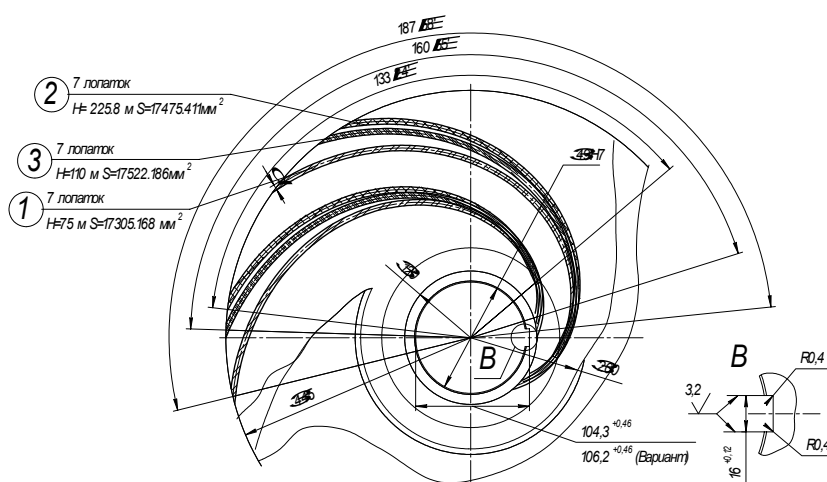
Планы лопастей рабочих колес насоса типа АЗЕ-630.75, АЗЕ-630.110 и АЗЕ-630.225/5245
